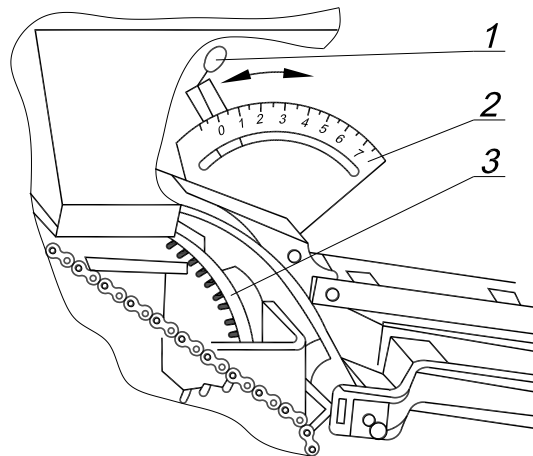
Механізм регулювання однозернового висіву сівалок типу УПС:
